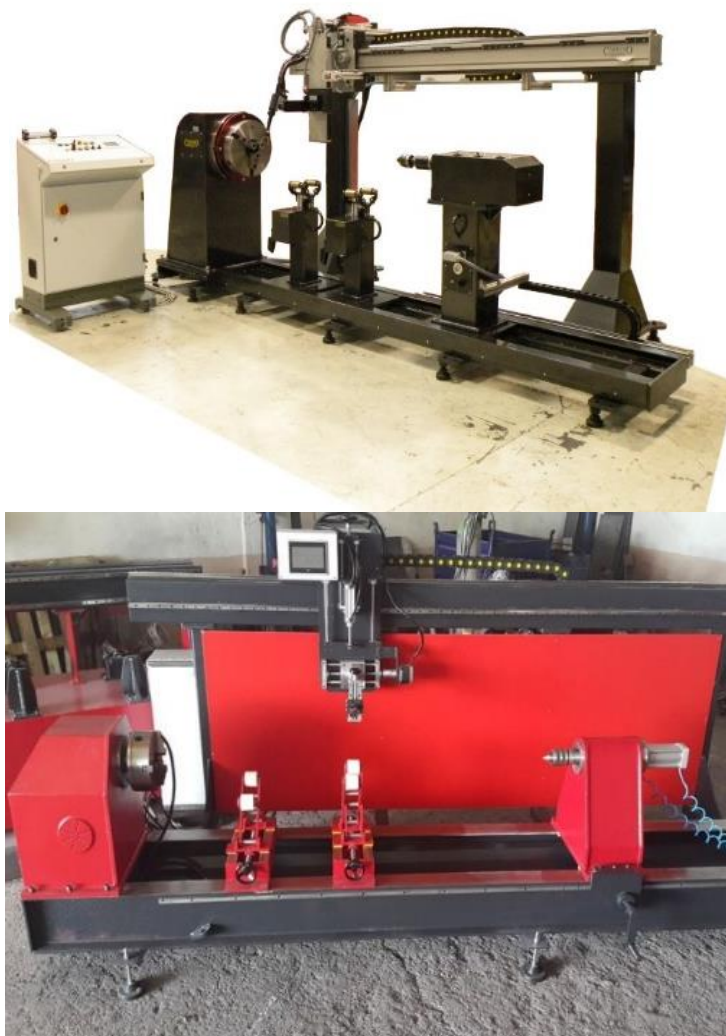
Зварювальні установки Joda Horizontal італійського виробника Carpano Equipment [1] та WWDKM-1000 турецького виробника WelkonWelding [3]
